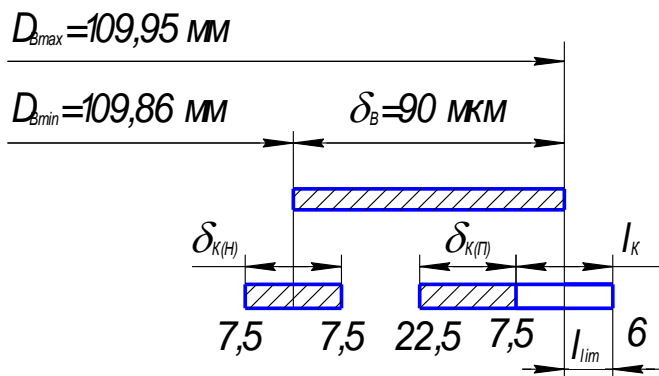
Положение полей допусков калибра относительно предельных размеров изделия.
